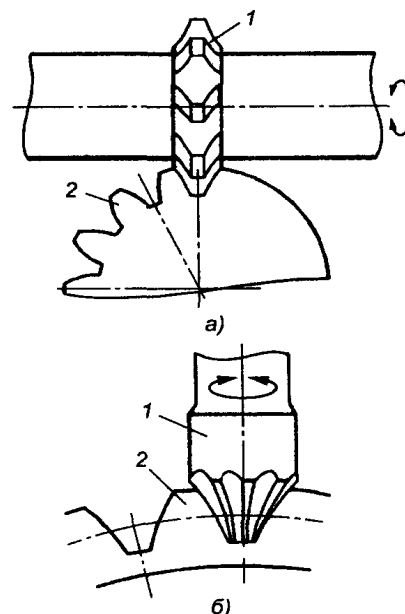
Схема нарезания зубчатых колес фрезой методом копирования: а — дисковой; б — пальцевой, 1 — фреза; 2 — заготовка
